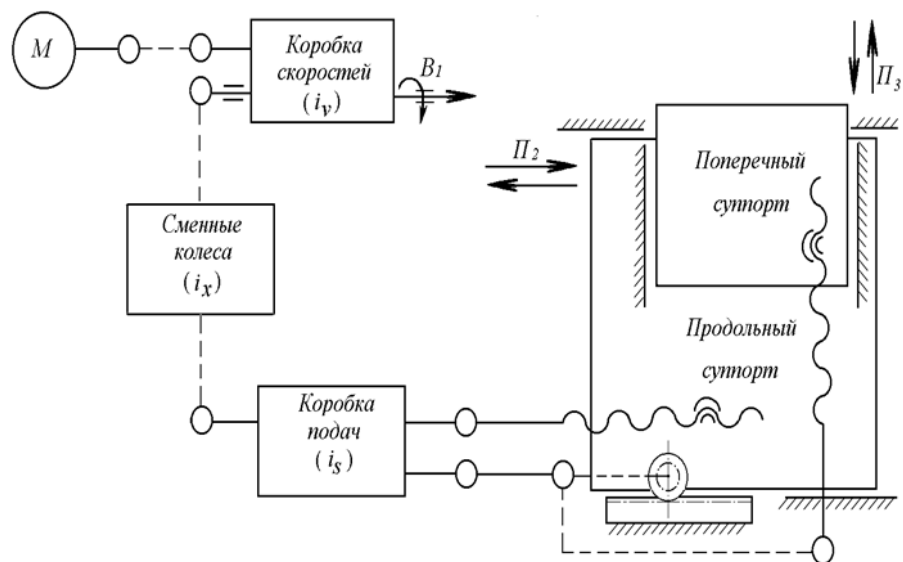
Принципиальная схема кинематических связей токарно-винторезного станка
